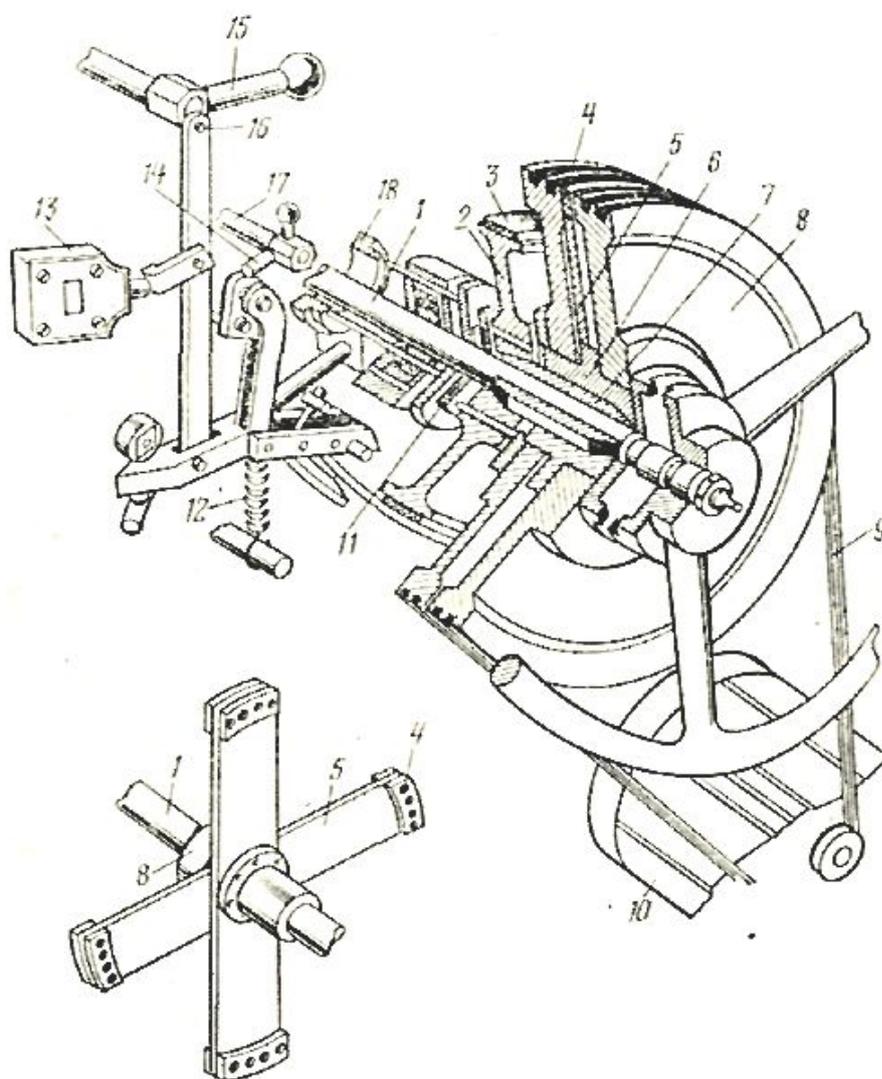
Привод станка СТБ: 1- главный вал, 2- тормозной шкив(барaban) 3- тормозная лента, 4- фрикционные пластины, 5- крестовина муфты, 6- фрикционная муфта сцепления, 7- разрезная конусная втулка, 8- шкивы, 9- клиноременная передача, 10- электродвигатель, 11- пластина рычага, 12- пружина, 13- конечный выключатель, 14- пусковая штанга, 15- рукоятка, 16- тяга, 17- вал контроллеров, 18- вилка.
